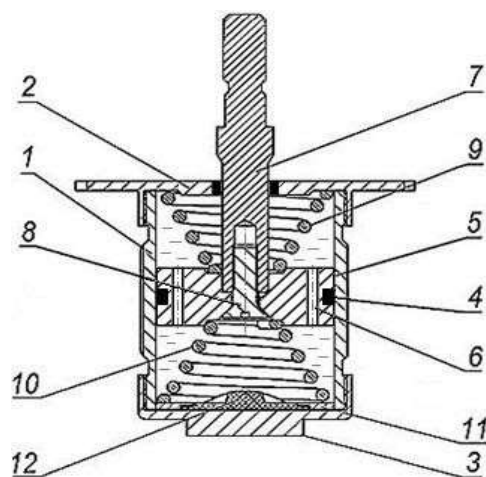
Устройство механического виброизолятора: 1 – корпус; 2 – фланец; 3 – крышка; 4 – уплотнительное кольцо; 5 – поршень; 6 – дросселирующее отверстие; 7 – шток; 8 – винт; 9 – верхняя коническая пружина; 10 – нижняя коническая пружина; 11 – диск; 12 – буфер
